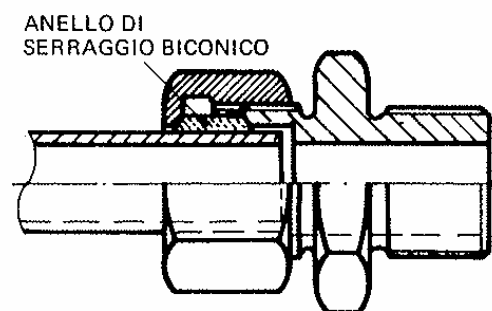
Giunto a bocchettone con anello di serraggio.
